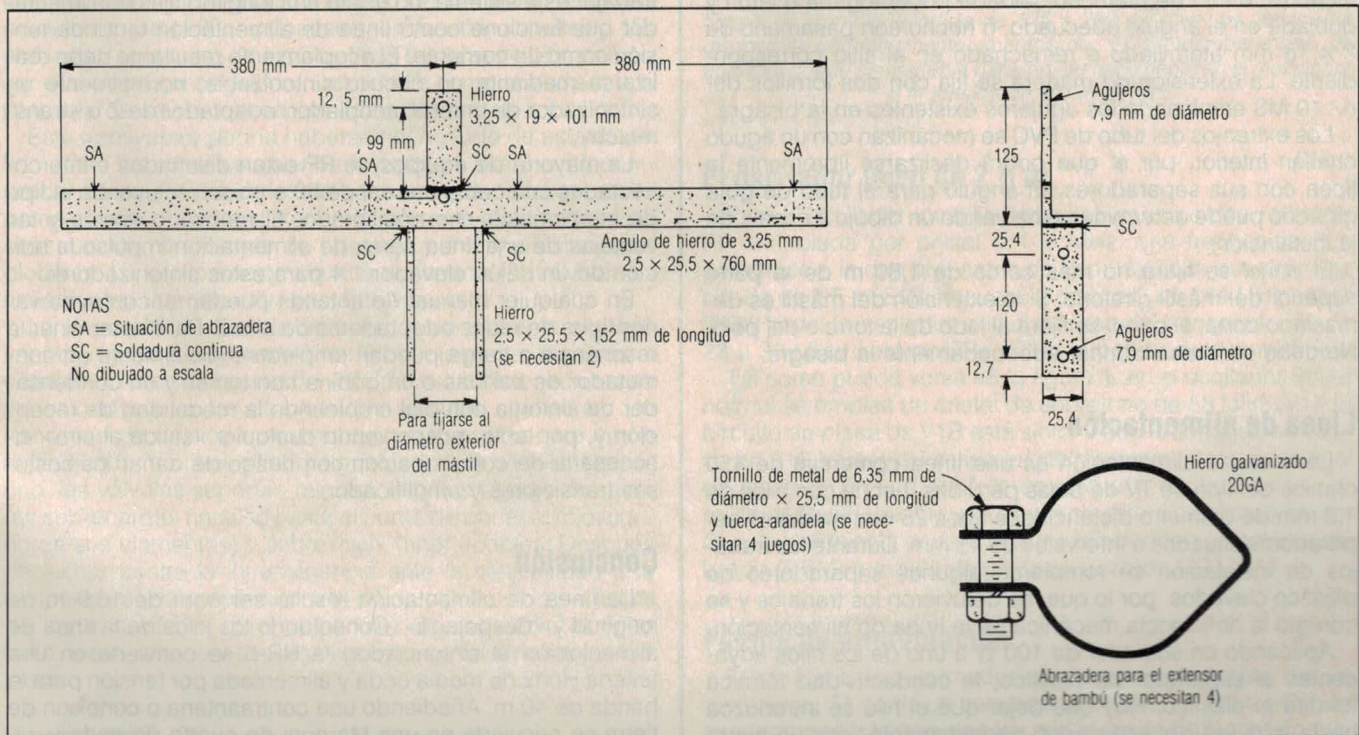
Detalles constructivos del dispositivo de montaje del extensor, el pilón, el mástil y las abrazaderas del extensor.
